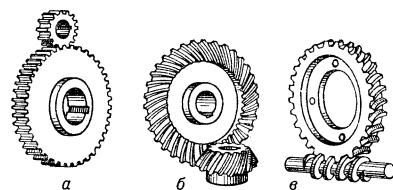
Передачи: а — зубчатая цилиндрическая; б — зубчатая коническая; в — червячная.
